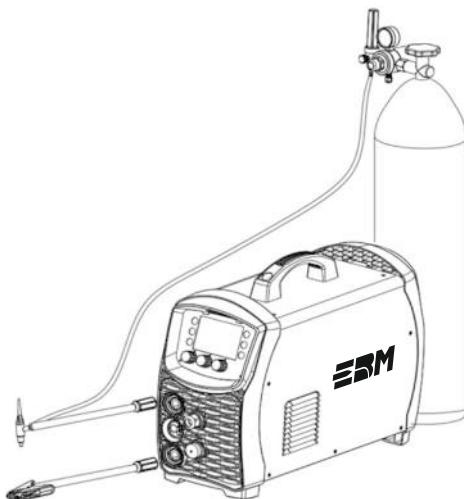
Схема подключения кабелей для TIG сварки
